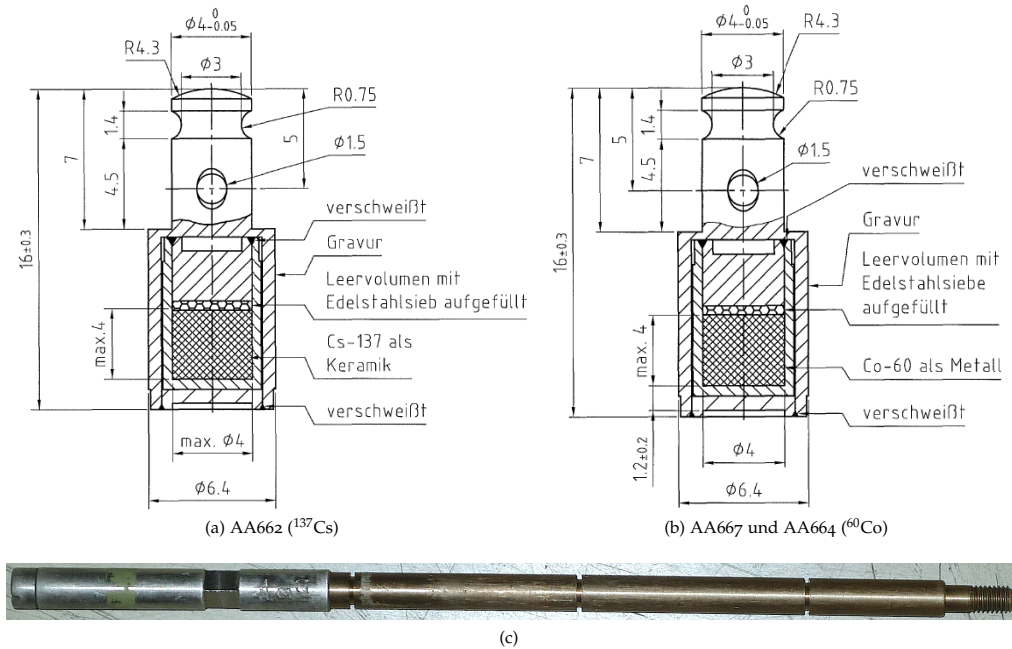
Technische Zeichnungen und Fotos der Referenzprüfstrahler für die experimentelle Validierung von SGsreco mit einem Testfassabschnitt. Das Quellgehäuse ist durch ein Drehgewinde an einem Stab befestigt.
